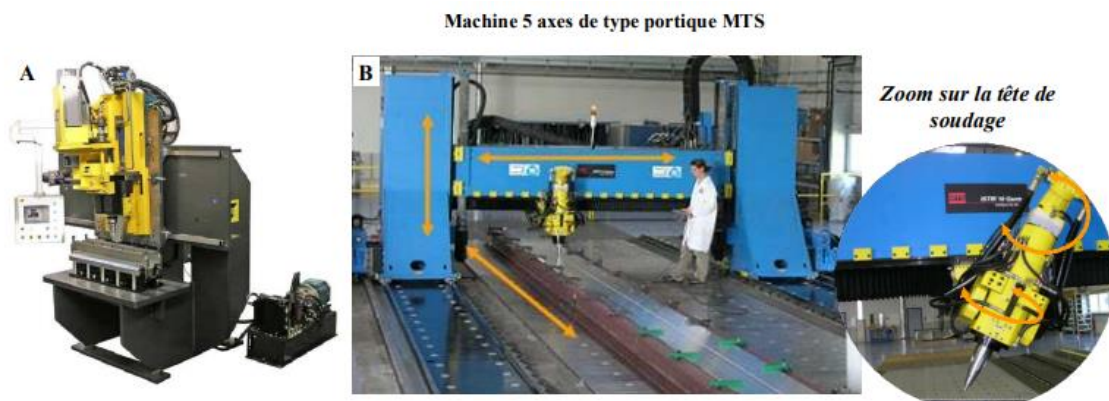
Exemple de machine dédiée au FSW. A- Machine ESAB Legio [2]
